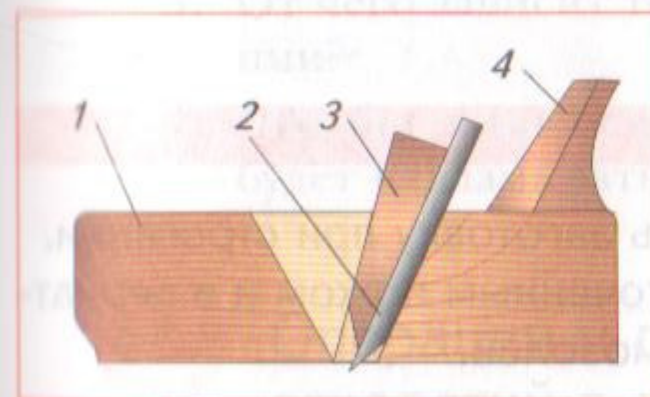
Устройство рубанка с деревянной колодкой: 1 — колодка; 2 — нож; 3 — клин; 4 — ручка
